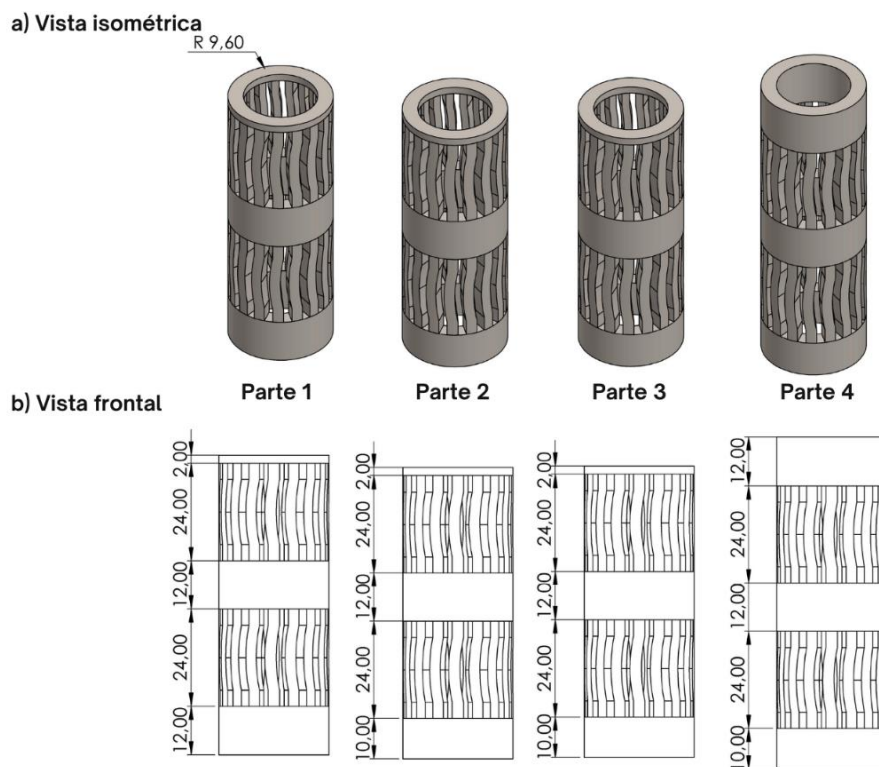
Divisão do CMM otimizado para impressão. Em a) Vista isométrica. Em b) Vista frontal
